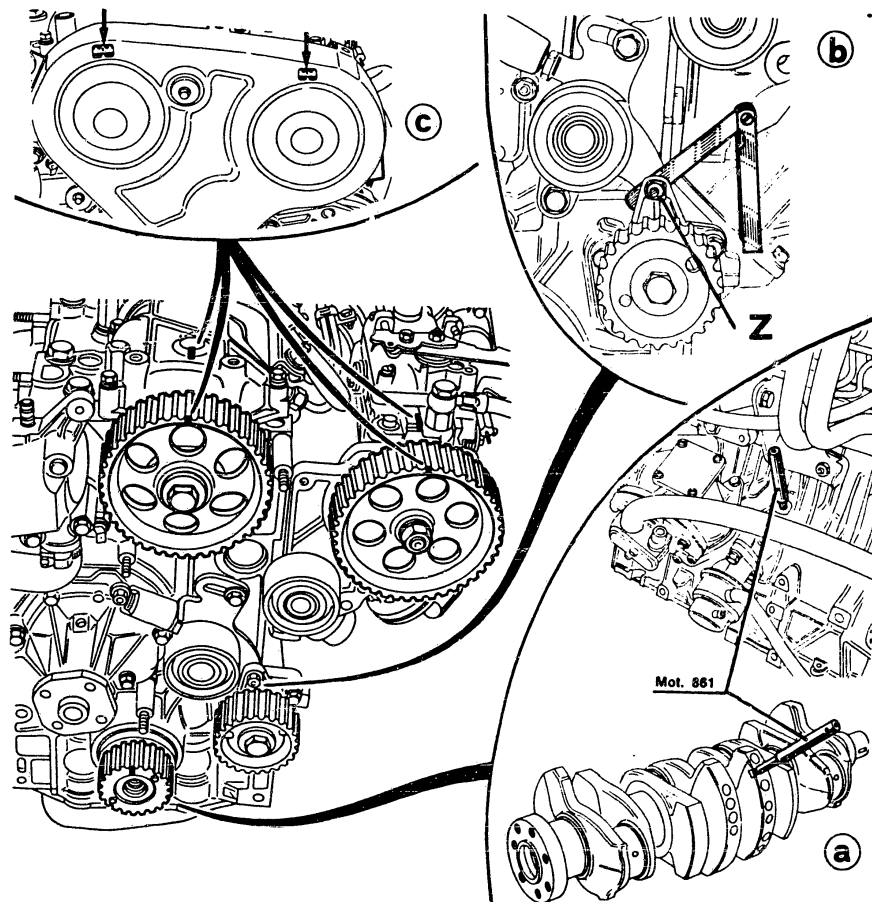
Einstellen der Motorsteuerung am Dieselmotor J8S: a) Die Kurbelwelle ist mit einem 8mm-Dorn zu fixieren – b) Das Spiel des Spannrollenhalters ist mit der Einstellschraube Z auf 0,1mm einzustellen – c) Stellung der Steuerräder von Nockenwelle und Einspritzpumpe.
